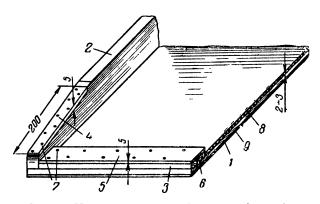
Усовершенствованный поднос (разрез). 1— основание; 2— боковые планки; 3— передняя планка; 4— защитная накладка; 5— то же; 6— шурупы; 7— гвоздики; 8— линолеум; 9— сукно или байка.
